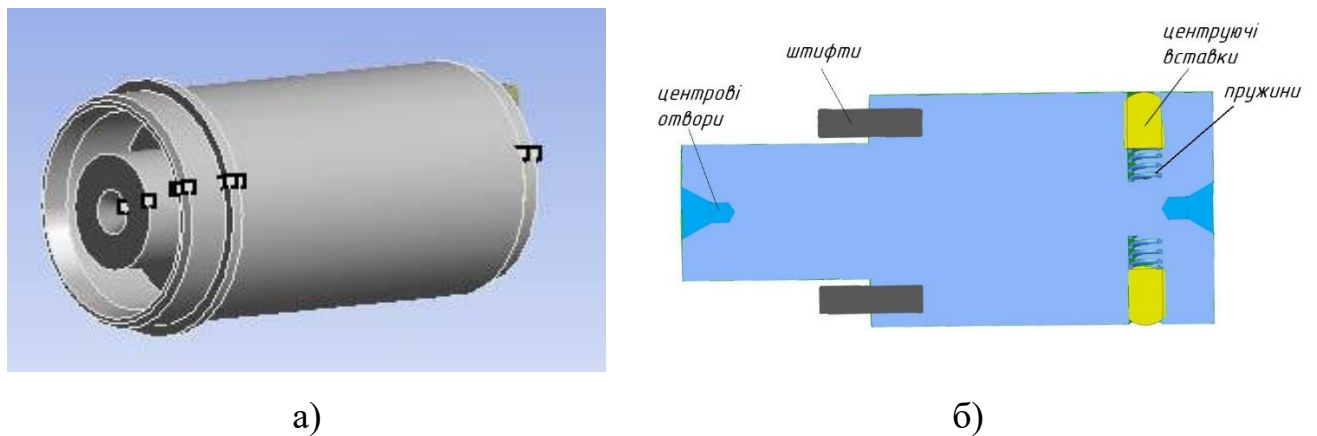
Спроектований верстатний пристрій для токарної обробки:
